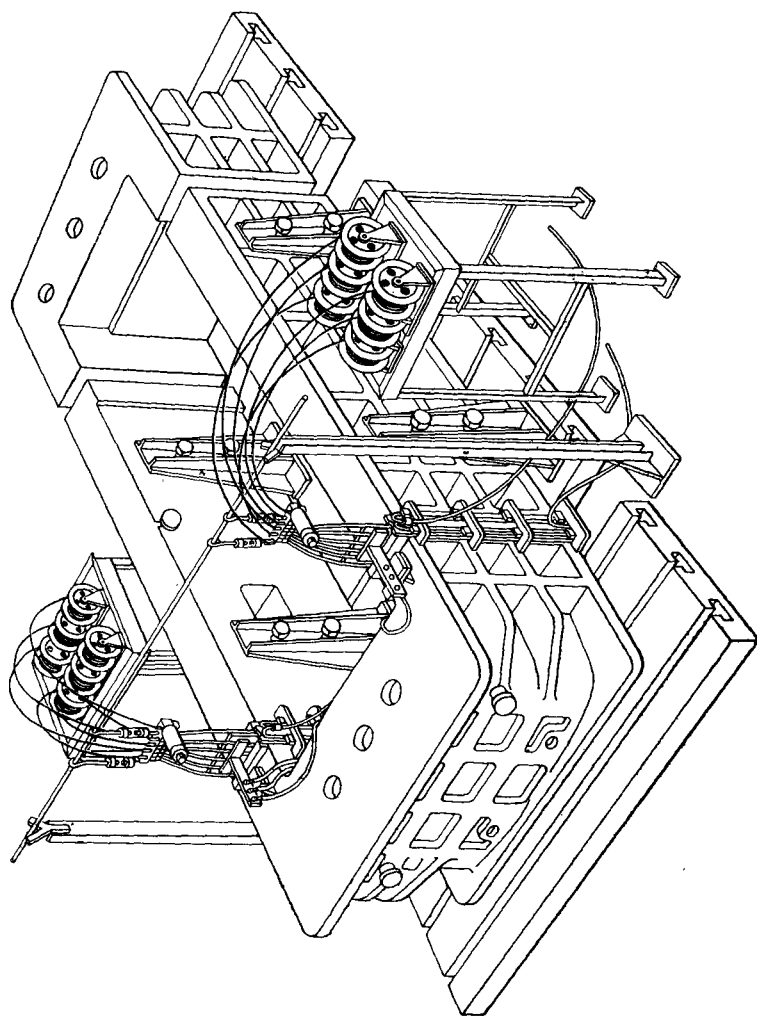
Рама щековой дробилки, собранная под электрошлаковую сварку плавающим мундштуком
